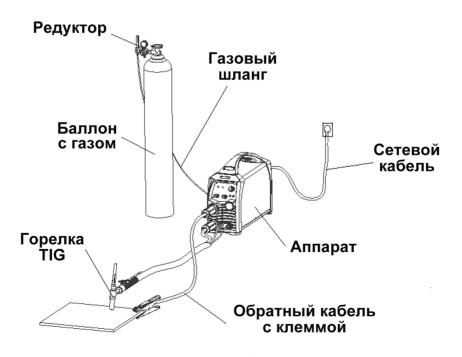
Схема подключения оборудования для TIG сварки
